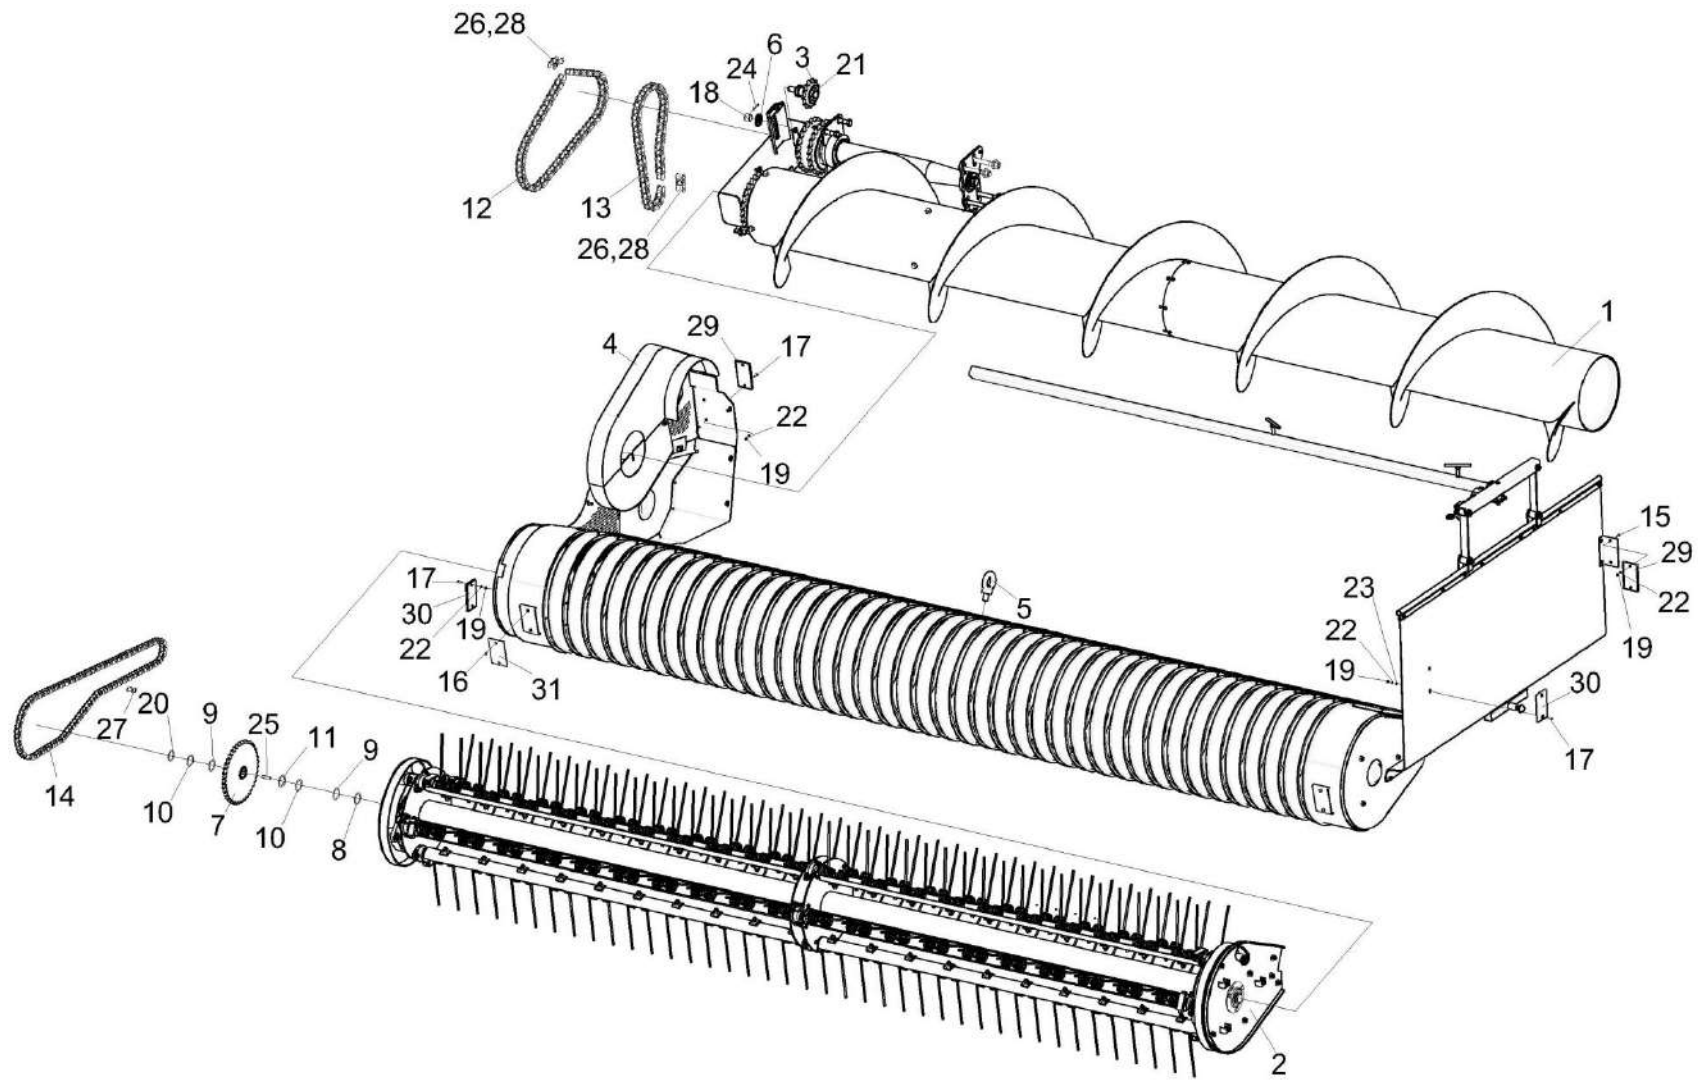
Валкооборачиватель КС-100-4900000 (лист 1)
